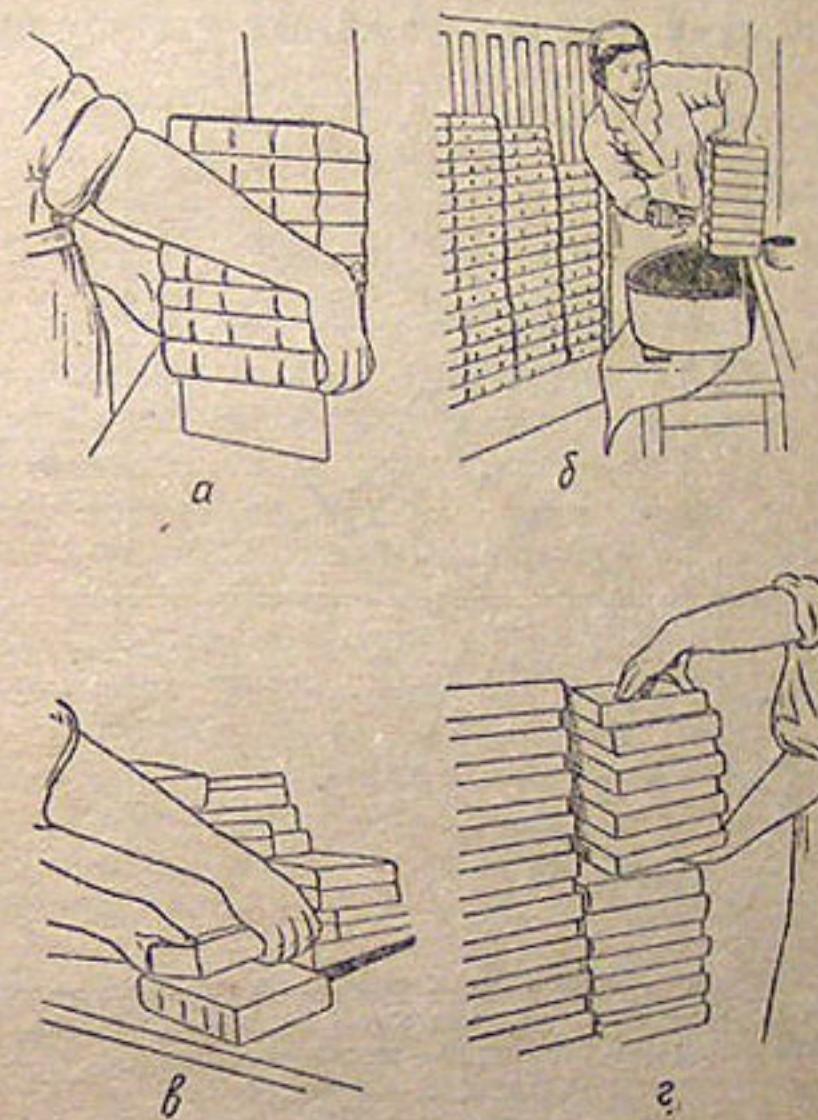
а. Процесс заклейки: а — укладка из угольника; б — промазка корешка; в — разборка блоков; г — укладка на фуру.
